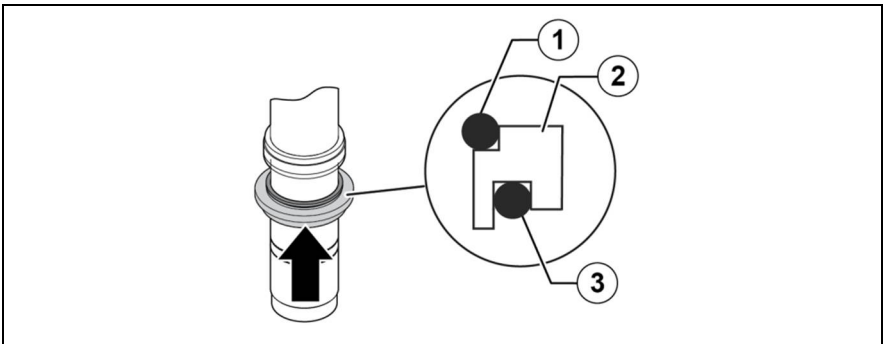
O-Ring-Halterung auf den Sensorkörper aufschieben
